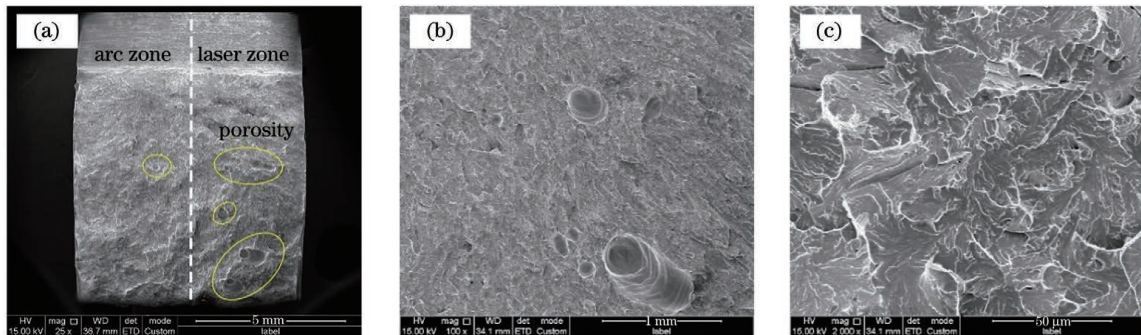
焊接速度为 0.8 m/min 时焊缝的冲击断口形貌。(a)宏观断口形貌;(b)小孔型气孔;(c)解理断裂
